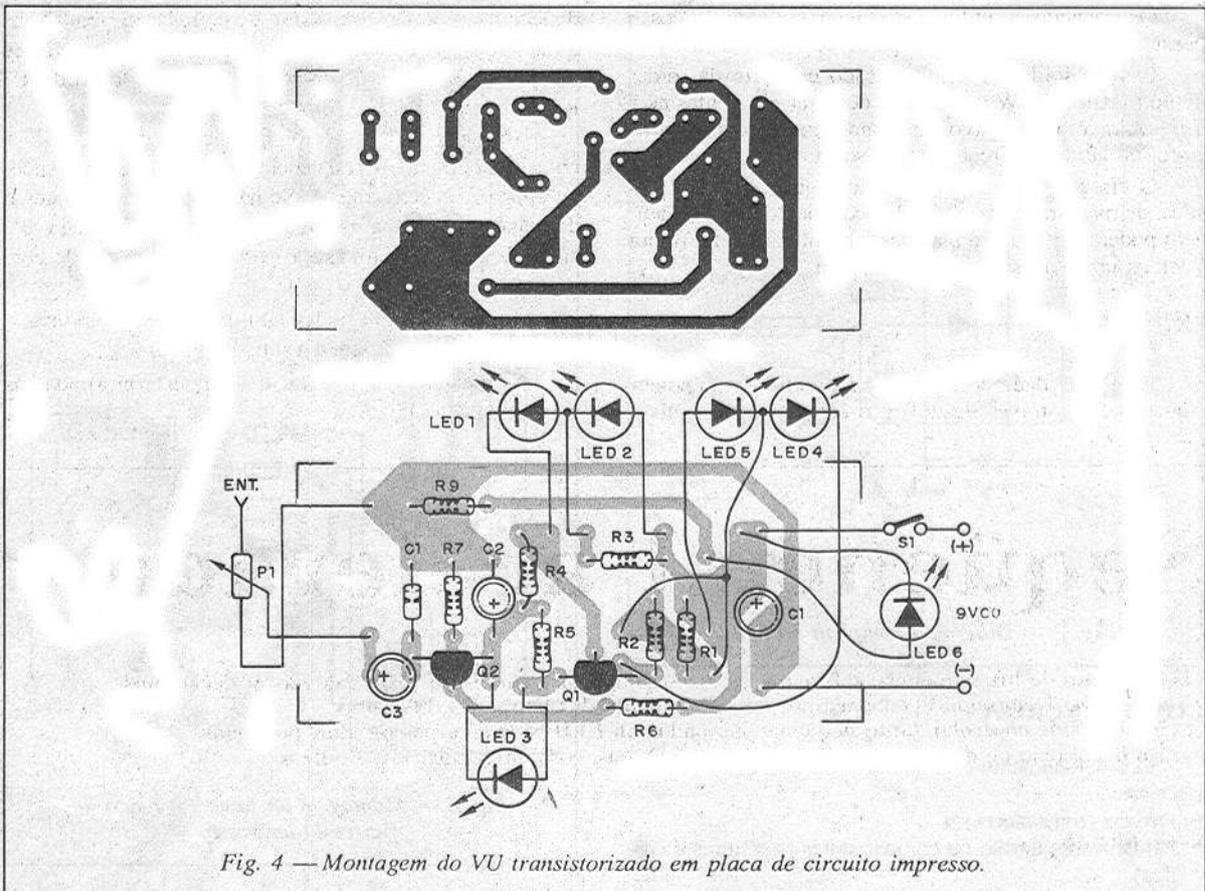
Montagem do VU transistorizado em placa de circuito impresso.
